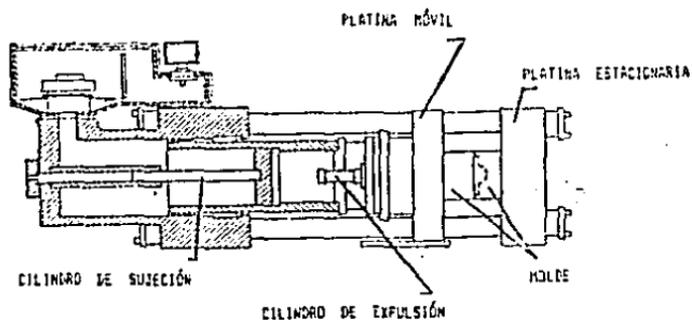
Unidad de cierre de una máquina de moldeo de materiales termoplásticos por inyección con sistema hidráulico.
